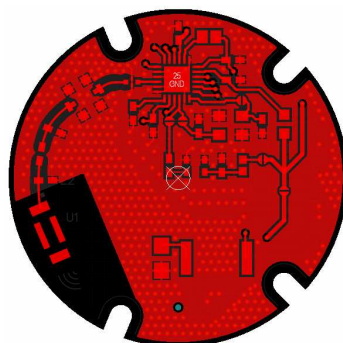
Vista 3D da camada inferior (BOTTOM) da PCB A2 LoRa.
